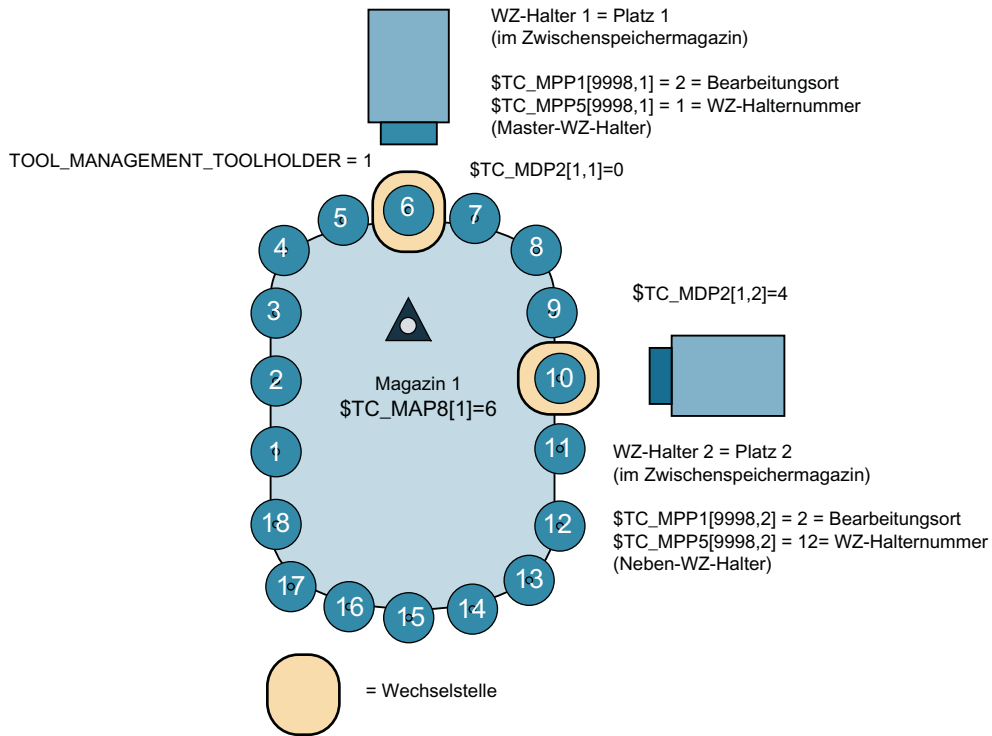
1 Kanal mit 2 Werkzeughaltern
